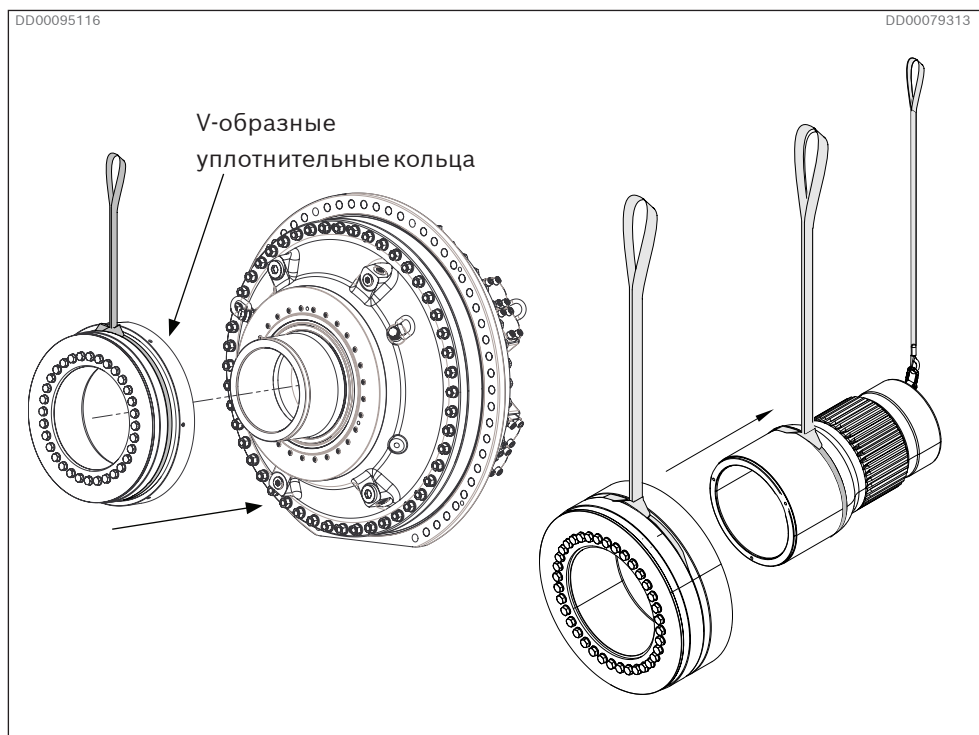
Монтаж муфты на адаптер вала или мотор, оснащенный муфтой
